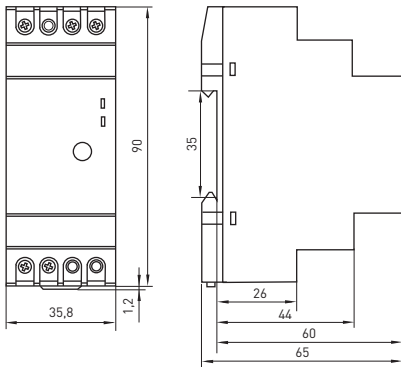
Габаритные размеры фотореле DIN-1 (ФР)
